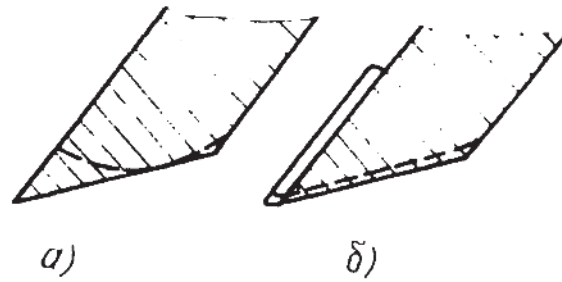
Схема изнашивания режущей кромки ножа скрепера:
